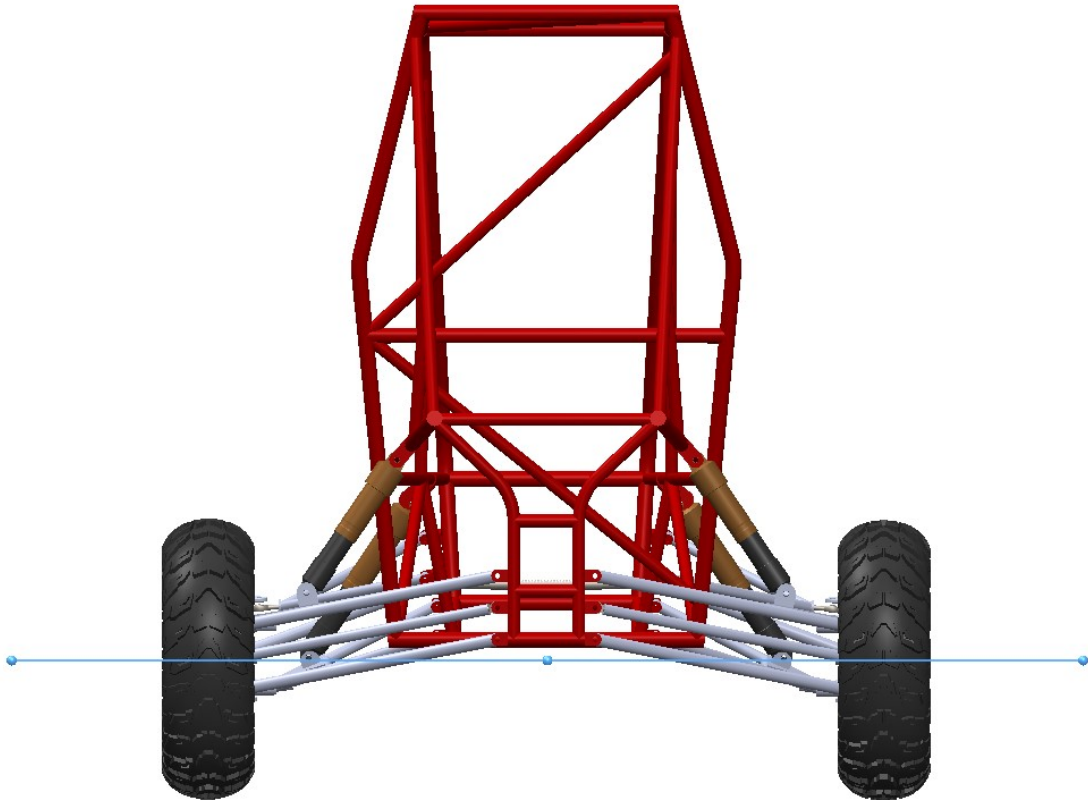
Posição dos elementos da suspensão traseira do primeiro ensaio
